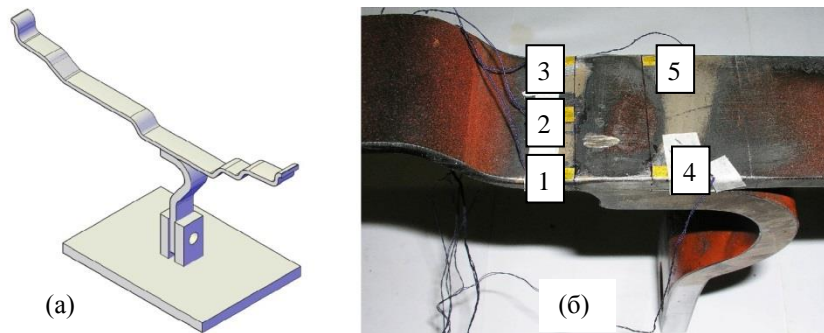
Эскиз закрепления и внешний вид образца-темплета колеса (а) с установленными и пронумерованными тензорезисторами (б)
